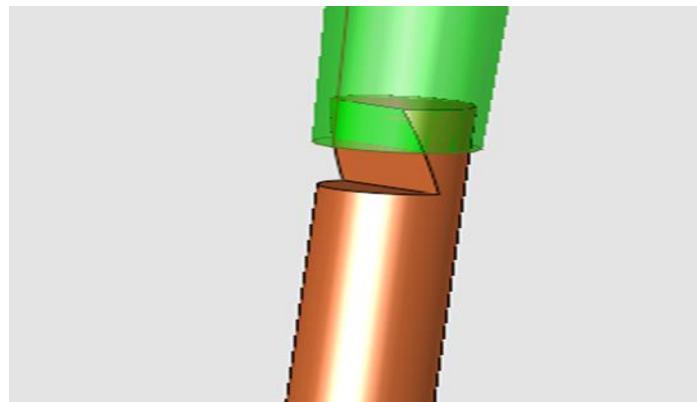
Bố trí chốt đẩy kênh dẫn
